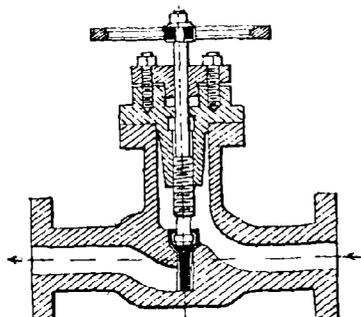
Robinet de réglage des machines à AzH^3 .
